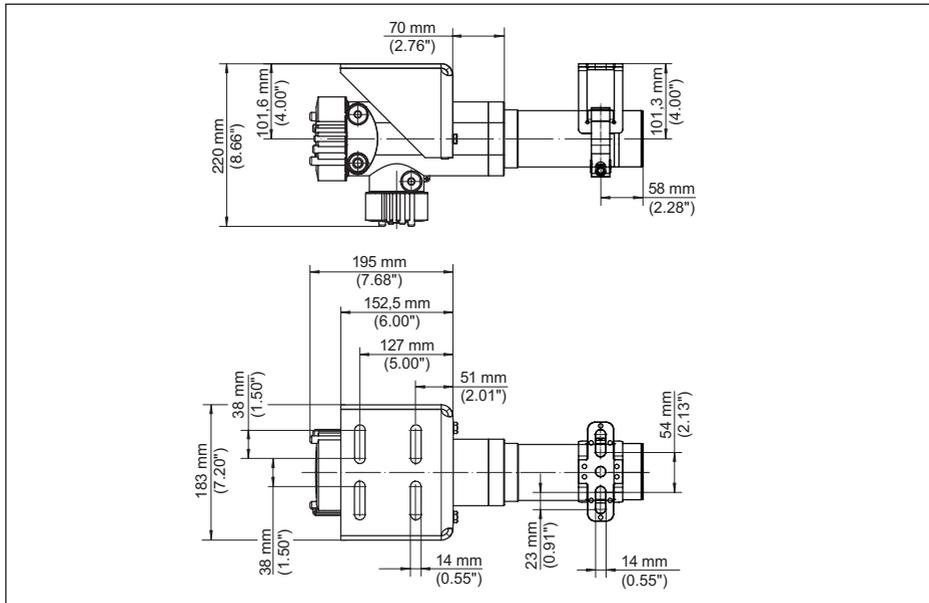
POINTRAC 31 com tubo do detector, 152 mm ou 304 mm (6 in/12 in) - com acessórios de montagem fornecidos juntos
